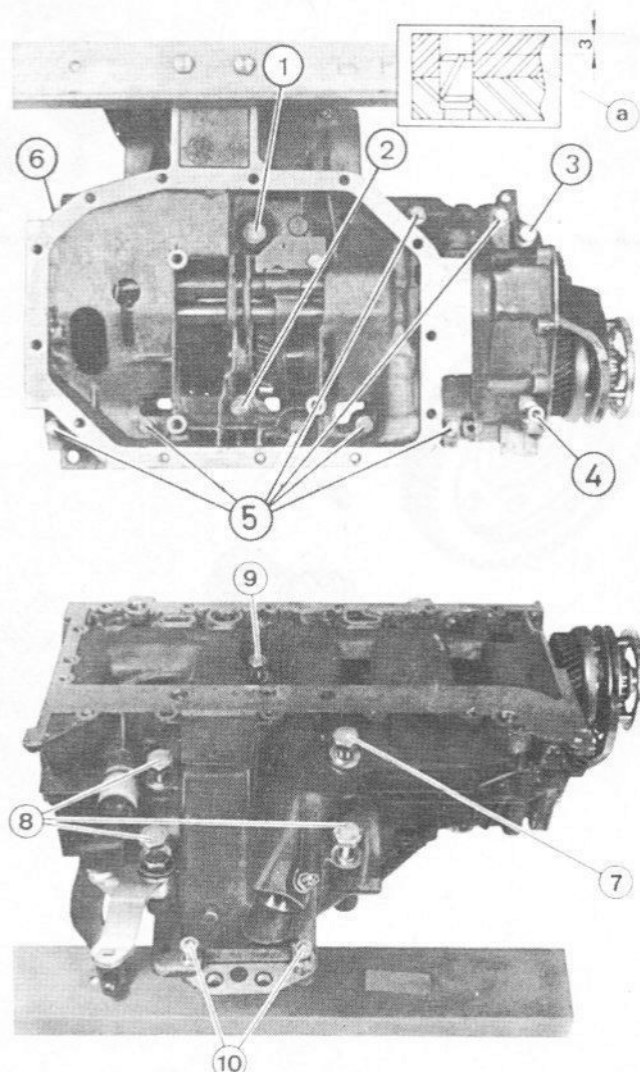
Positions des boulons de connexion du carter de boîte (Sec 10)
